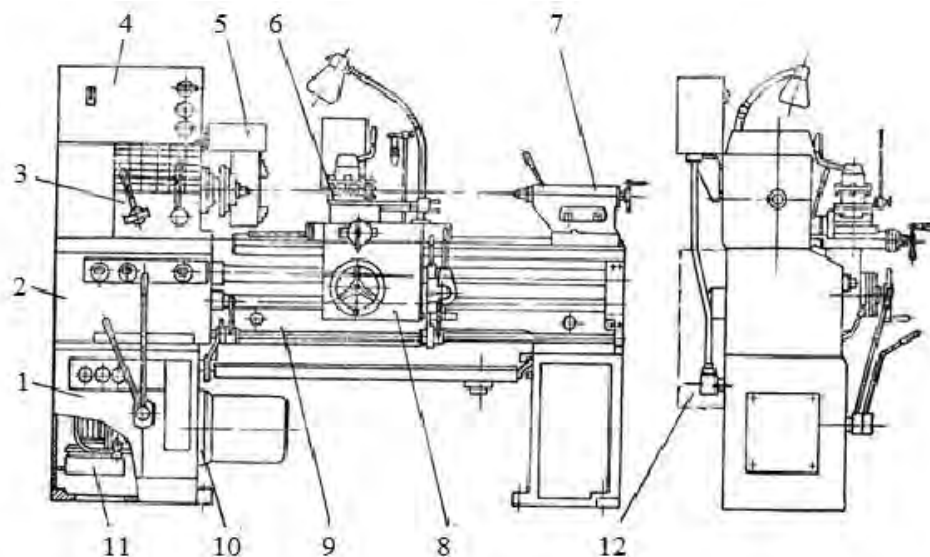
Токарно-винторезный станок модели ИТ-1М:
